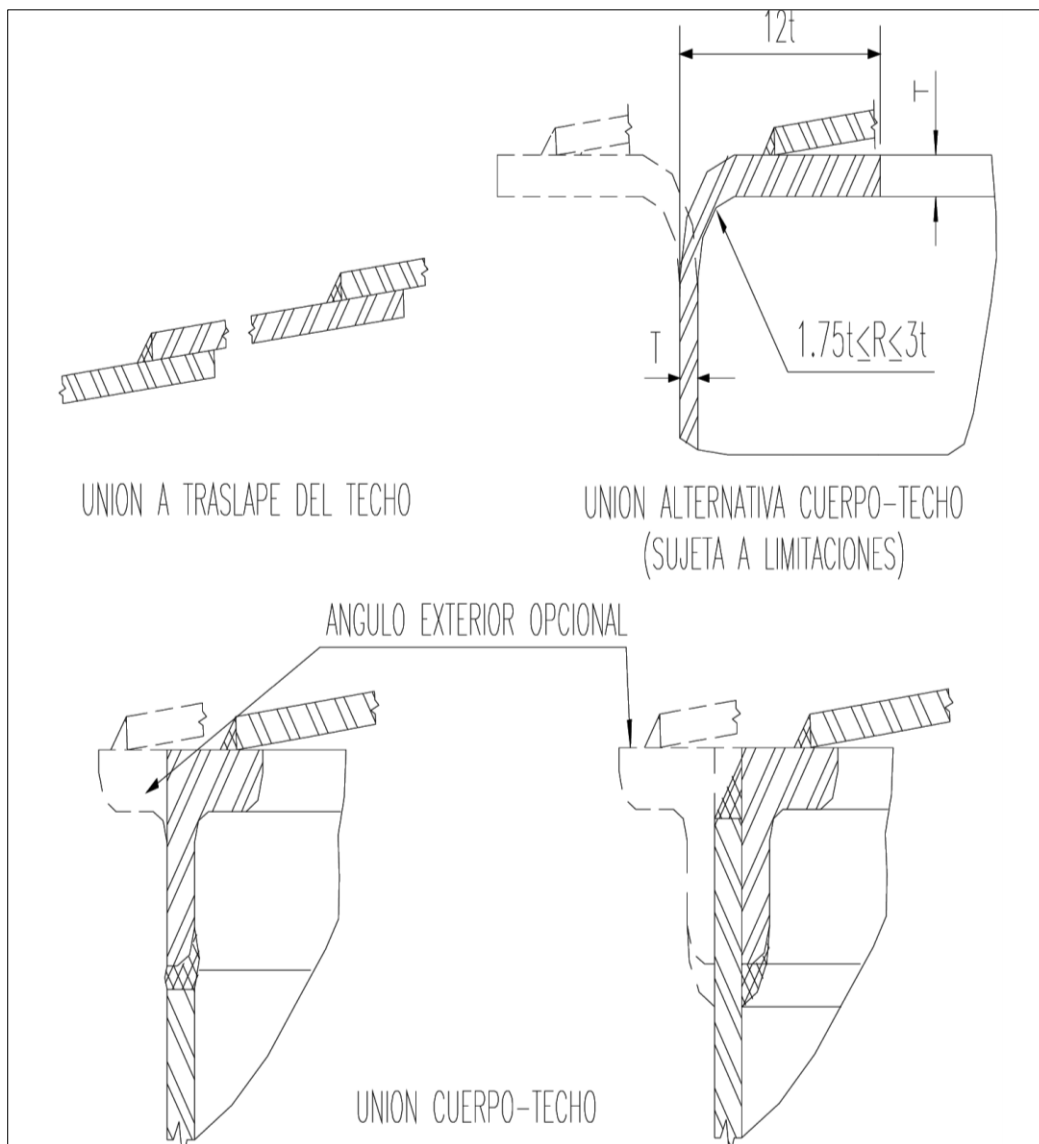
Detalles Típicos de Soldadura del Techo.
